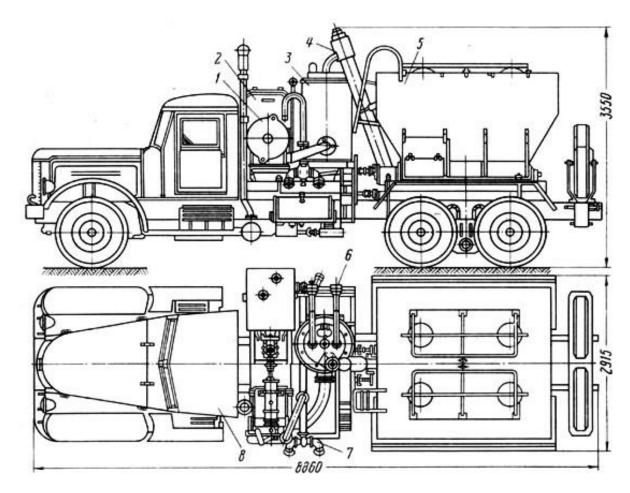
Пескосмесительный агрегат ЗПА: 1 - центробежный насос 4ПС; 2 - силовой блок двигателя ГАЗ-51; 3 - смесительное устройство;4 - наклонный шнек; 5 - бункер для песка; 6 - приемный трубопровод;
